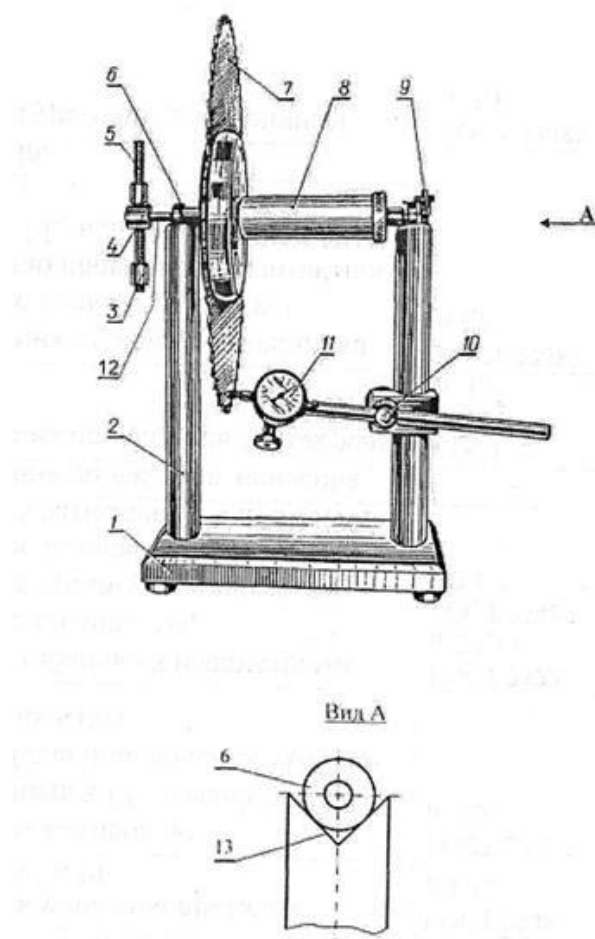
Пристрій для вимірювання дисбалансу інструменту
